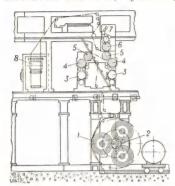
Схема секцип ротапионного газетного агрегата ГА: 1 — рулон бумаги; 2 — ролевая ввевда; 3 — основные красочные аппараты; 4 — формные цилиндры; 5 — печатные пилиндры; 6 — формный цилиндр второй краски; 7 — красочный аппарат второй краски; 8 — фальцевальный аппарат. Пунктиром показан путь бумажного полотна.
